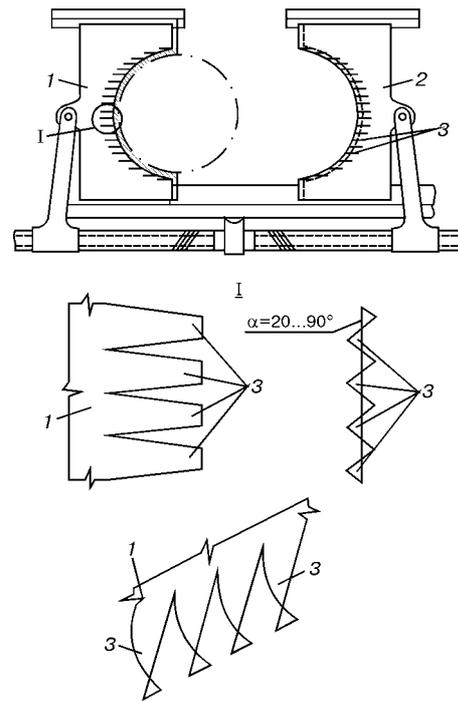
Схема устройства для сварки встык труб из термопласта (обозначения см. в тексте)
